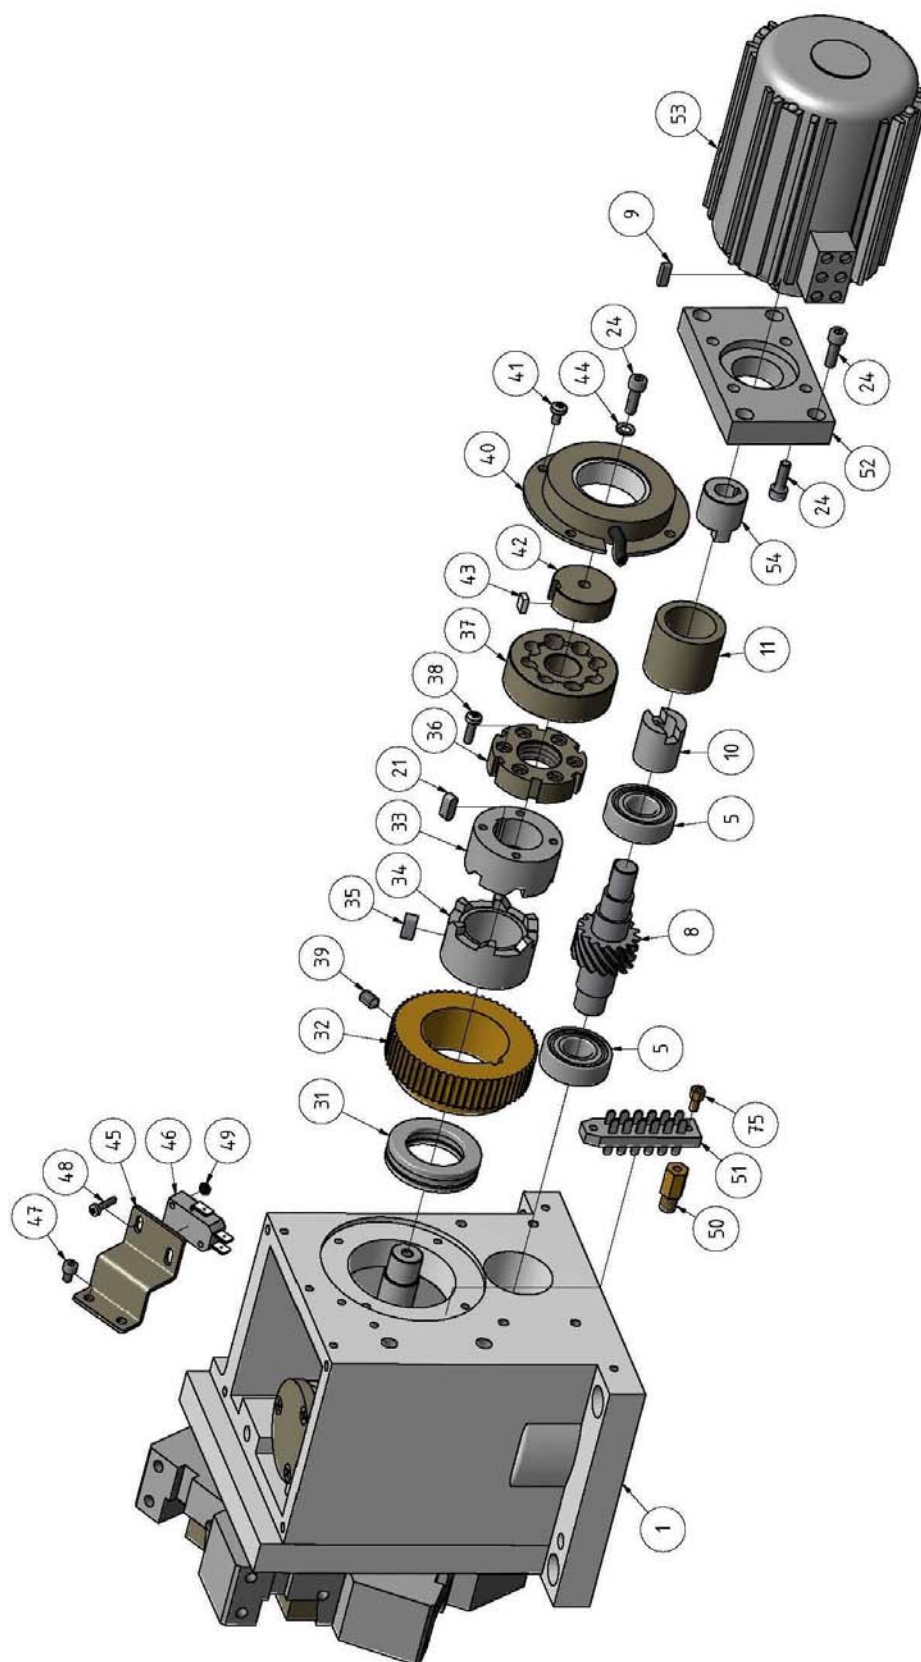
Werkzeugwechsler 1-2 - Tool changer 1-2
